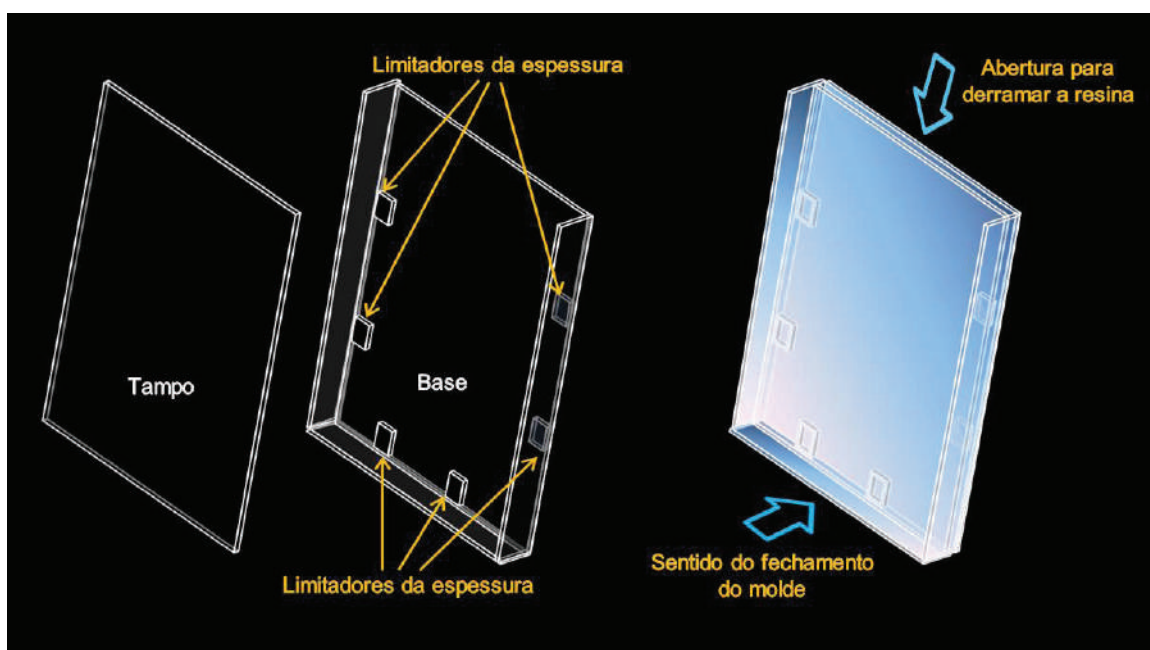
Partes e montagem do molde fechado para fabricação da placa RN+NPG.
